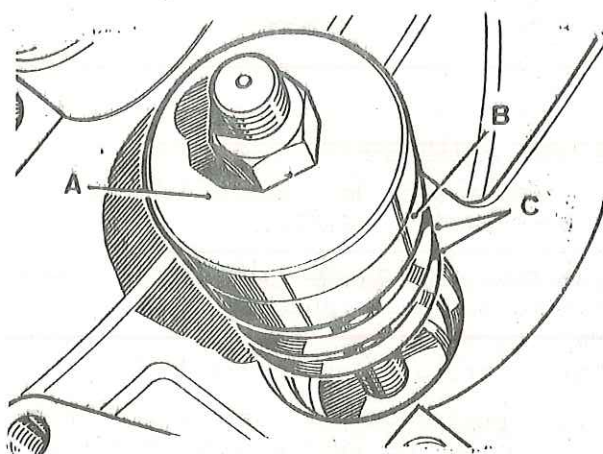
Arandelas-suplemento y montaje de la pista del cojinete de cabeza
